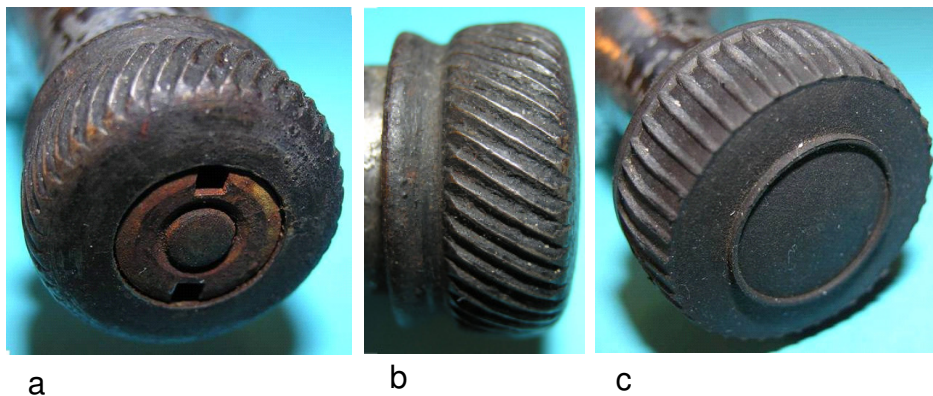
Reibrad (22 mm Durchmesser): a) Versenkte Schlitzmutter, b) Geschrägte Rippen und Schleuderkante, c) Gummikappe mit 31 mm Durchmesser
